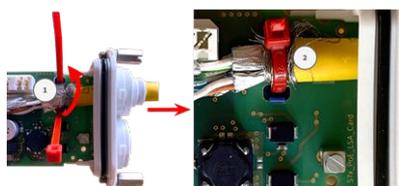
Fascetta serracavi inserita sotto il cavo di rete
